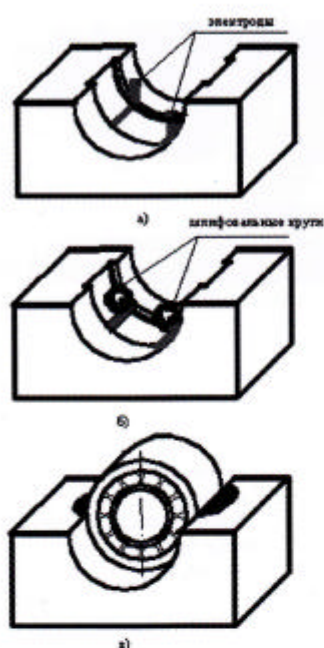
Подготовка, расположение установочных маячков, нанесение материала и установка подшипника в проектное положение
